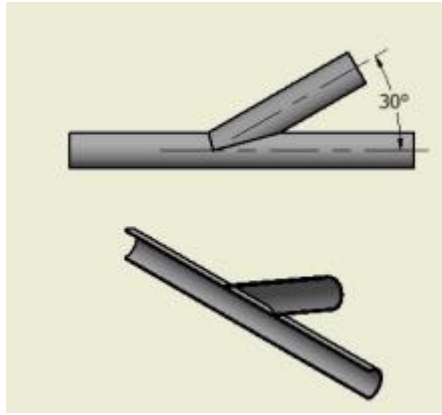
Chasis monocasco, Muestra de Soldadura 2. [1].
